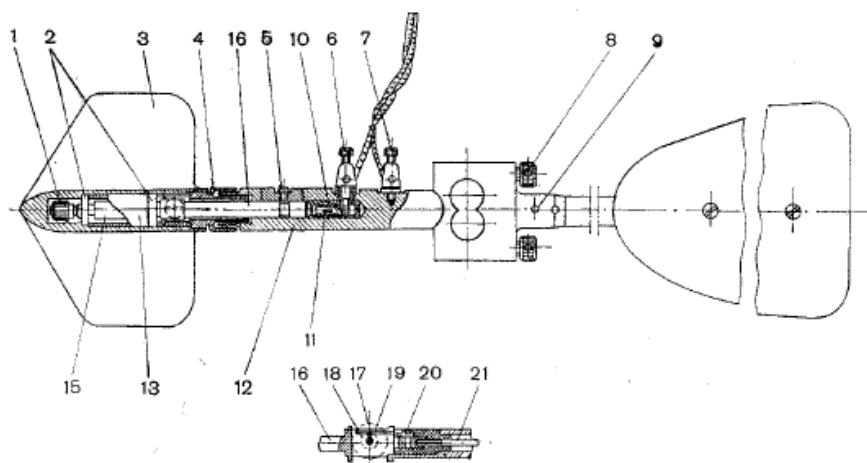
Общий вид вертушки ГР-21М (в разрезе).
